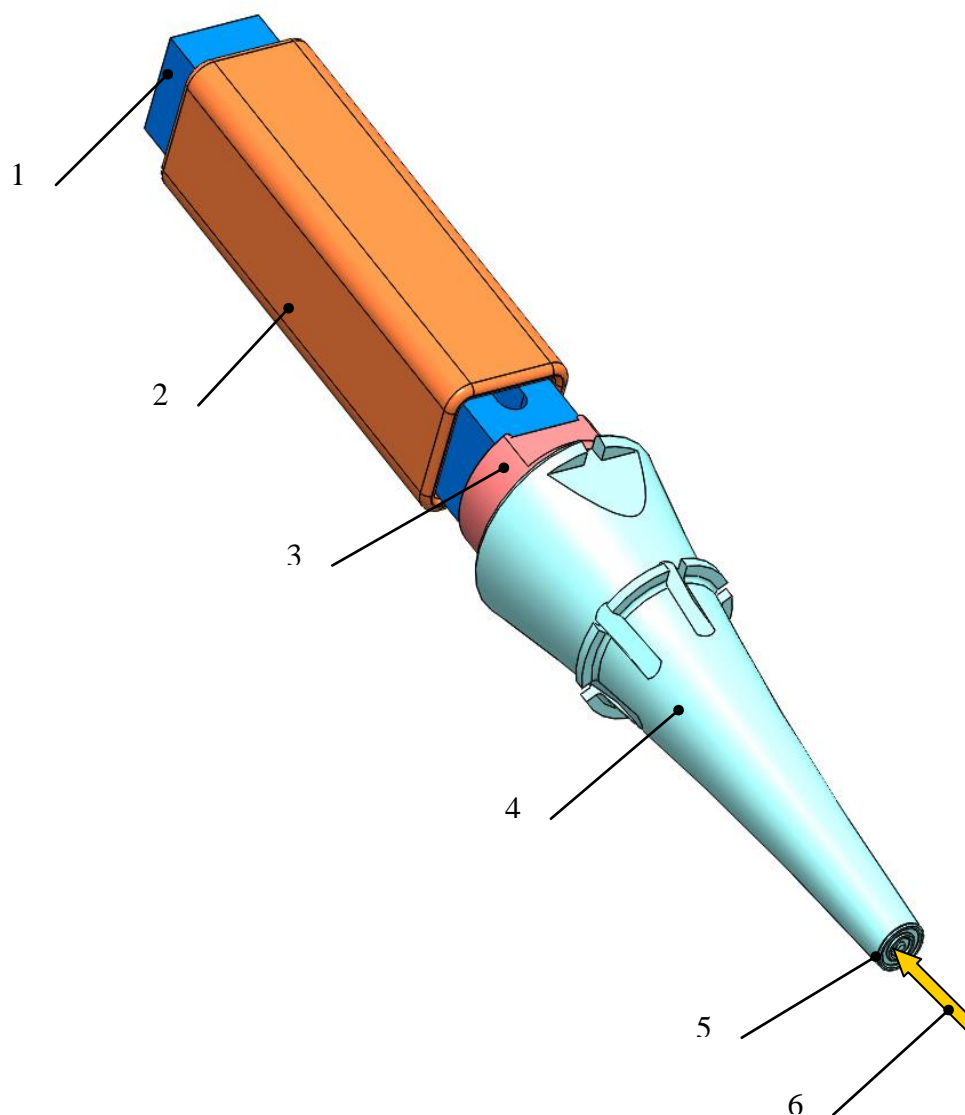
Общий вид УЗКС для ультразвуковой точечной сварки:
